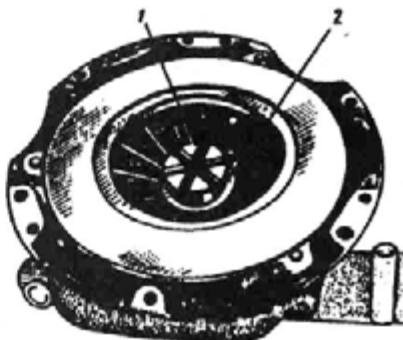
Установка приспособления для закернивания центральной втулки при сборке:
